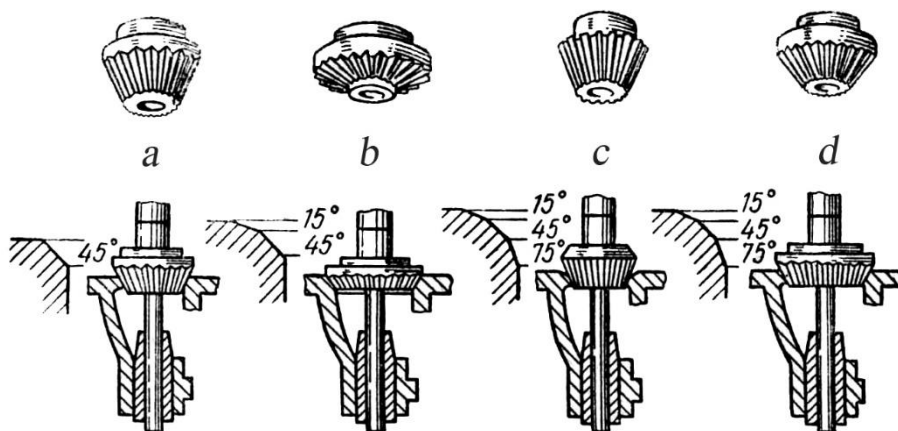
Обробка клапанного гнізда фрезами. Фрезерування під кутом: а – 45°; б – 15°; в – 75°; д – чистове під 45°
